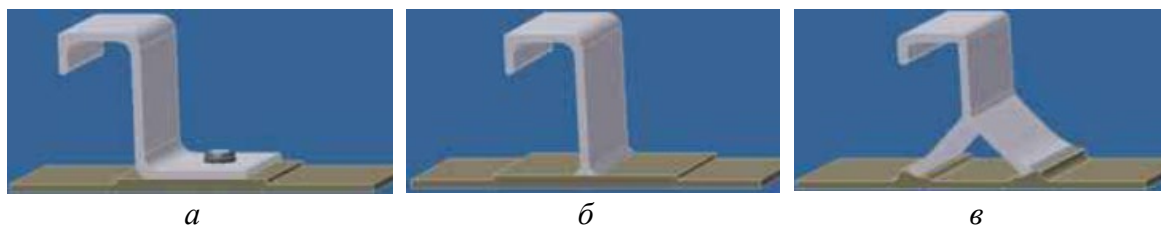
Схемы различных соединений стрингер – обшивка
